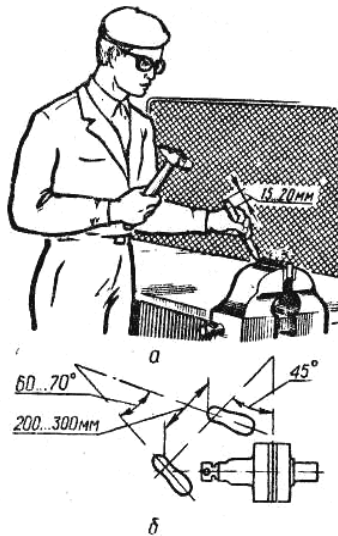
Положення корпуса (а) і ніг (б) під час рубання
